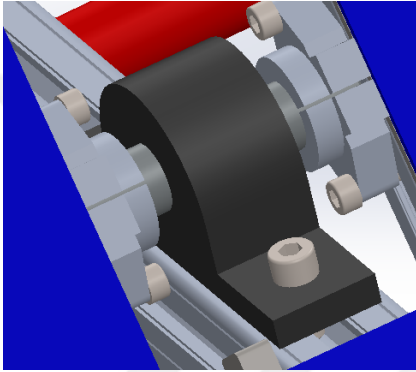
Ayna konstrüksiyonunda tutucunun kullanılması
